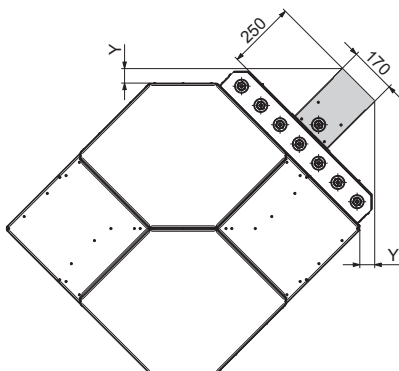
Maßbild Adapter für Gotthard Kombiblock (in mm)
